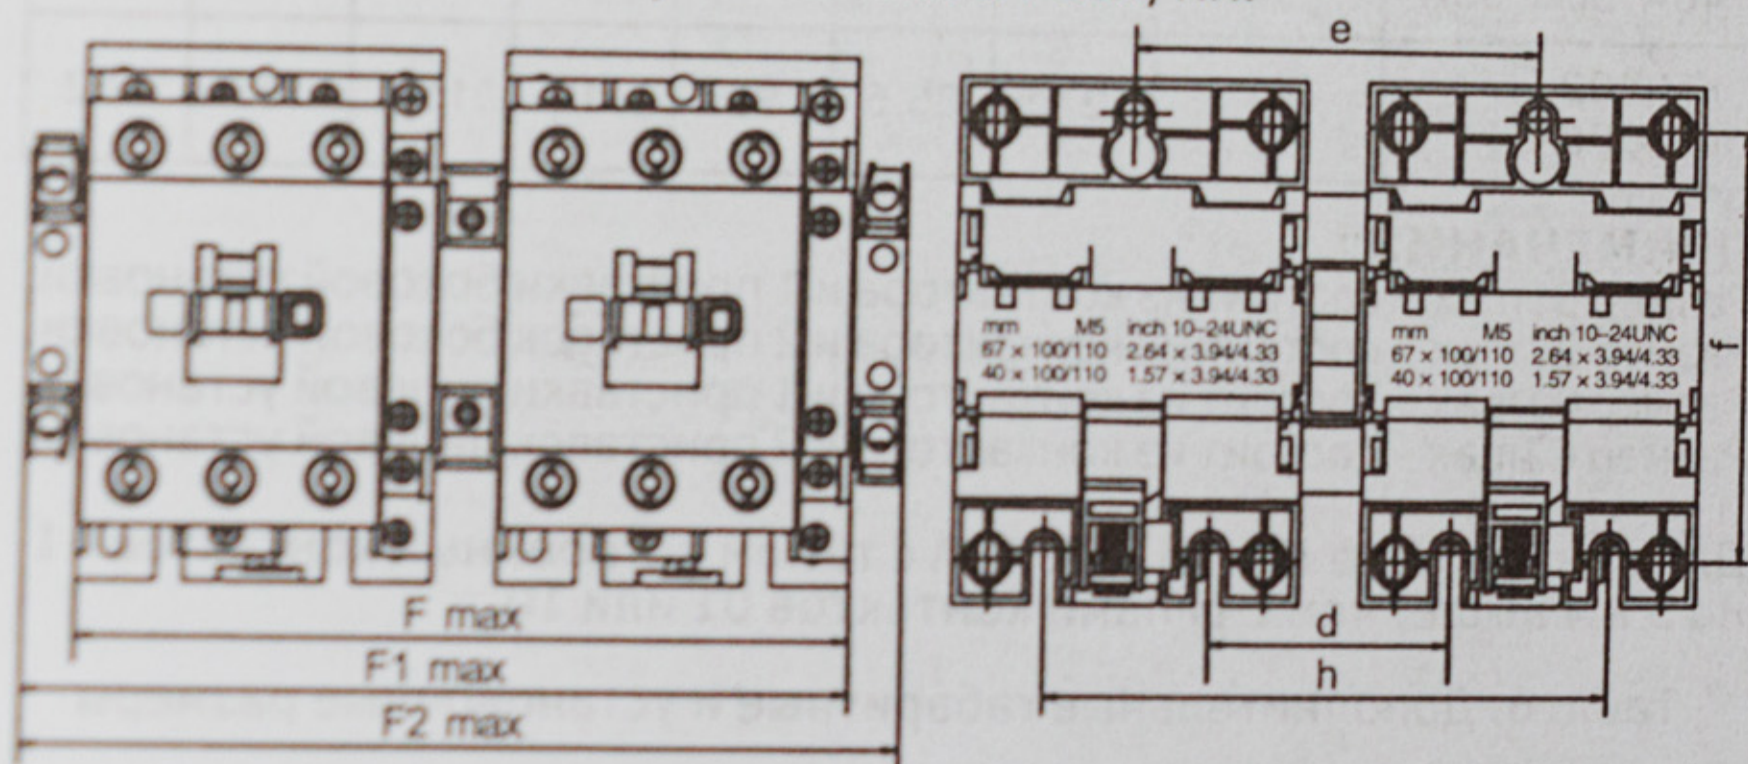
Габаритные и установочные размеры контакторов с реверсивной сборкой на токи 40А–95А, мм.
